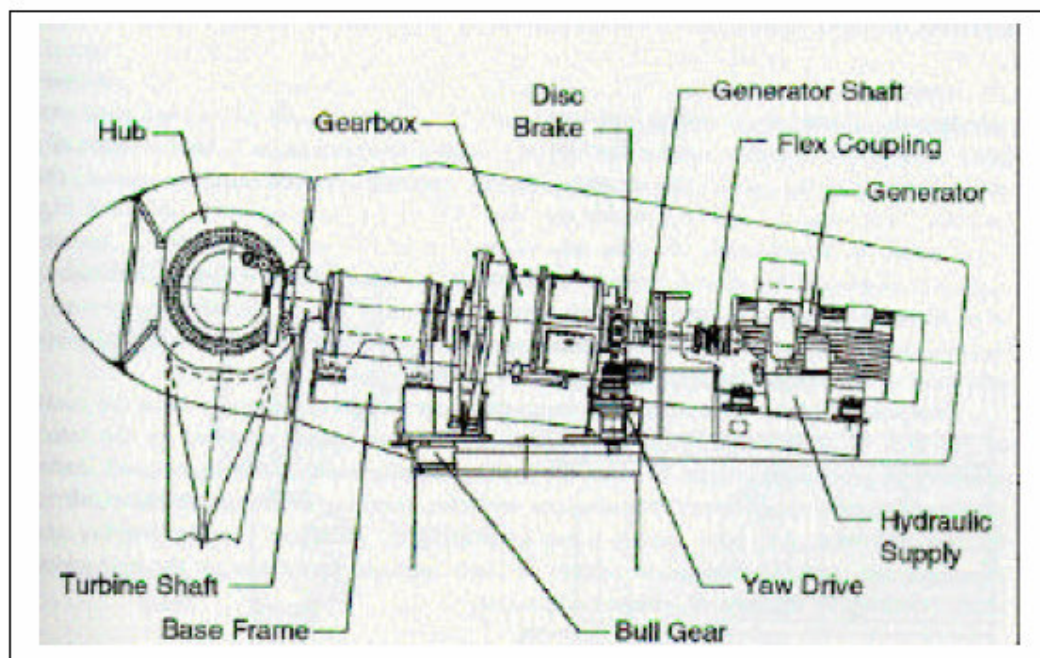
Detalhe de uma caixa de engrenagem
